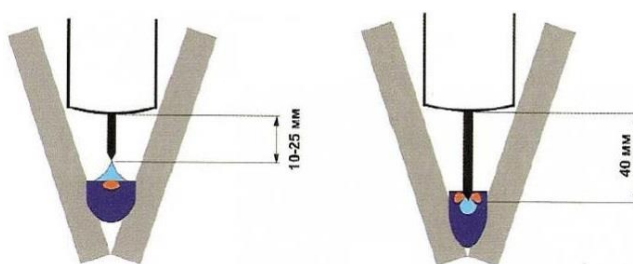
Вылет стандартной *MIG/MAG* проволоки и сварки по технологии *ForceArc
